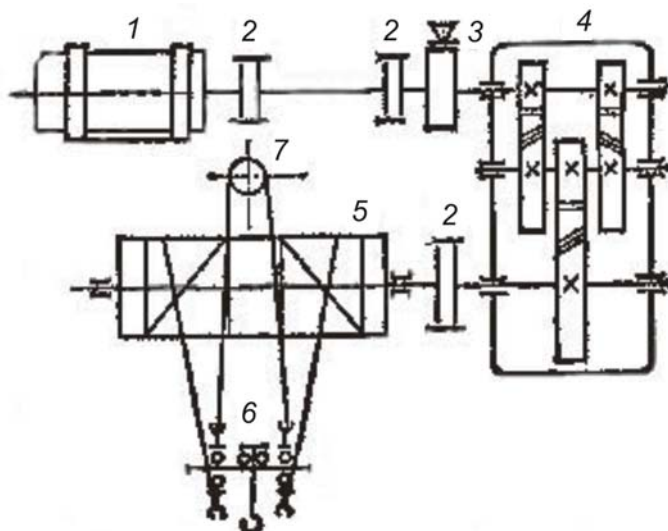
Кинематическая схема механизма подъема главного крюка: 1 — двигатель; 2 — муфта; 3 — тормоз; 4 — редуктор; 5 — барабан; 6 — полиспаст; 7 — неподвижный блок полиспасты
